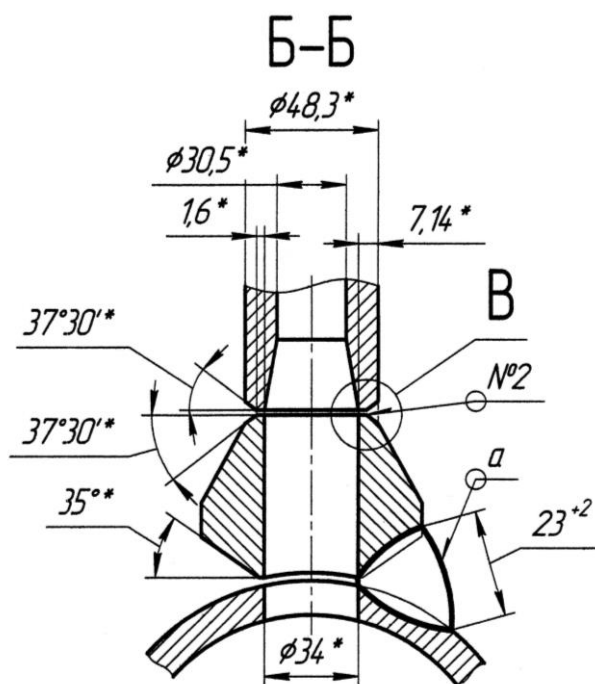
Общий вид соединения трубы 1 и бобышки 6 (сечение Б-Б).
